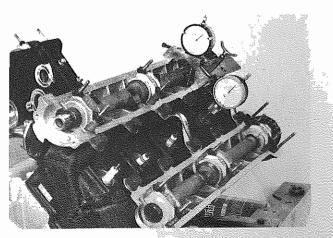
Montare il comparatore n. 42 Fit gauge No. 42
